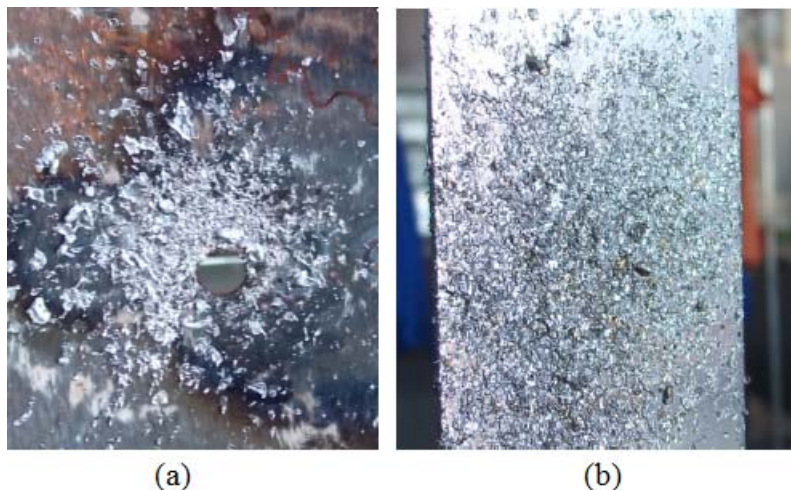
(a) Corpo de prova do primeiro teste e (b) Corpo de prova do segundo teste.
